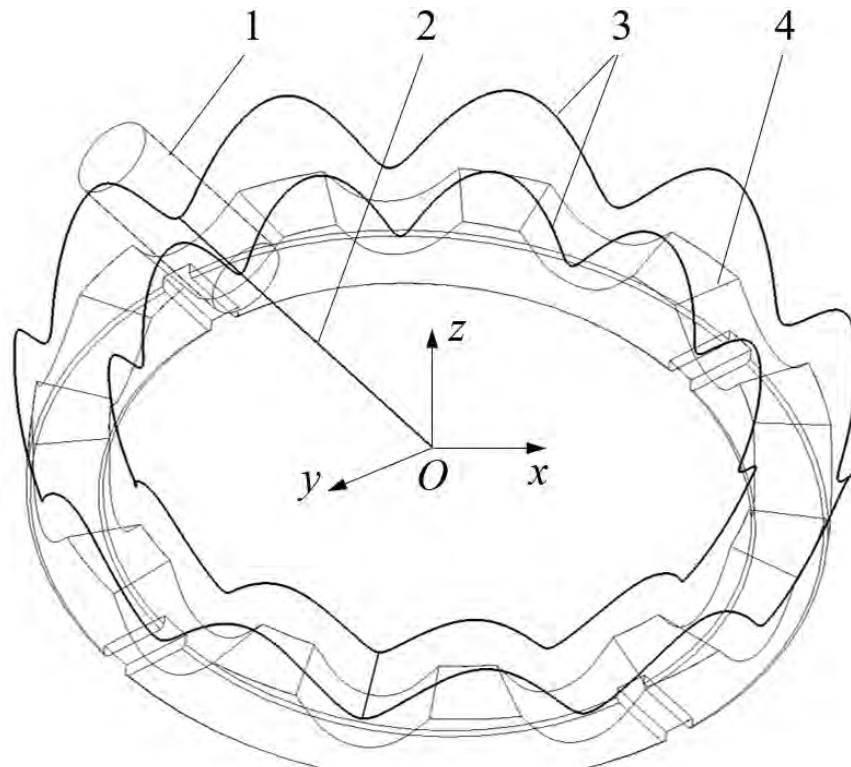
Траектории движения точек оси цилиндрической фрезы: 1 – инструмент (цилиндрическая фреза); 2 – ось инструмента; 3 – траектории крайних точек осей; 4 – зубчатый профиль
